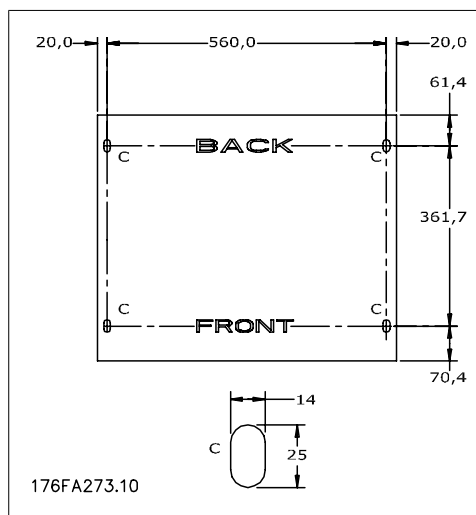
Чертеж для сверления крепежных отверстий в полу.
